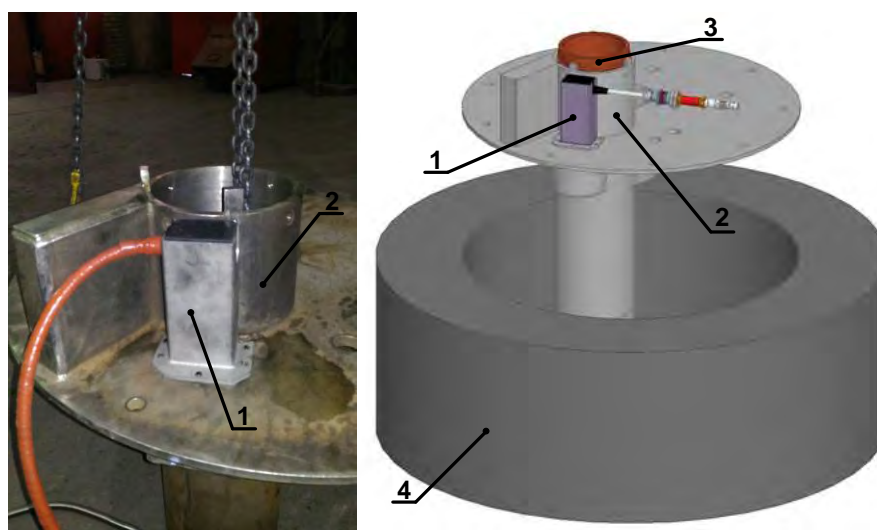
Датчик, установленный на рубашку из нержавеющей стали трубного кристаллизатора (Завод №2): 1 – датчик; 2 – рубашка из нержавеющей стали; 3 – медная гильза; 4 – корпус ЭМП
